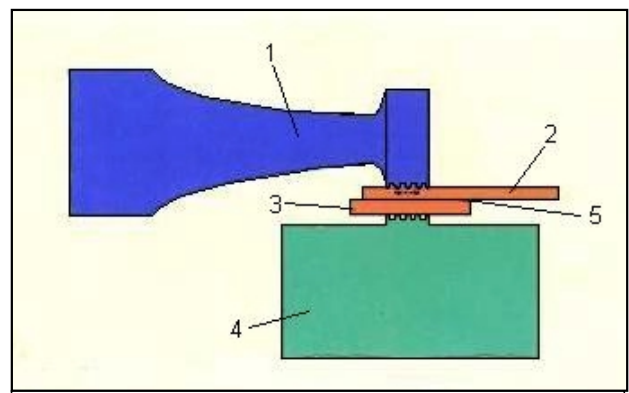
Esquema de un sistema típico de soldadura ultrasónica para metales. 1.- Sonotrode: transductor piezoeléctrico, fuente de la vibración ultrasónica, 2 y 3.- Partes a ser unidas, 4.- Yunque: plancha de acero, 5.- área a ser soldada
